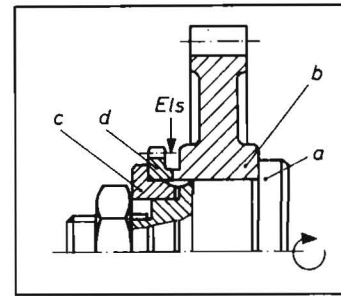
Schweißdorn für das Elektronenstrahlschweißen radial;
